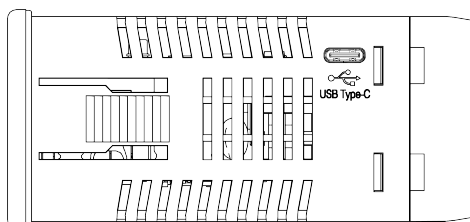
Расположение разъема USB для корпуса Щ5
